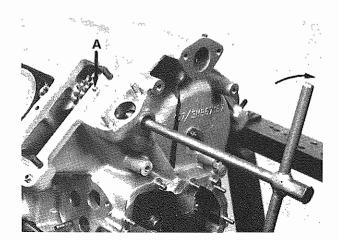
Estrattore n. 12 - A) Vite Puller No. 12 - A) Screw
